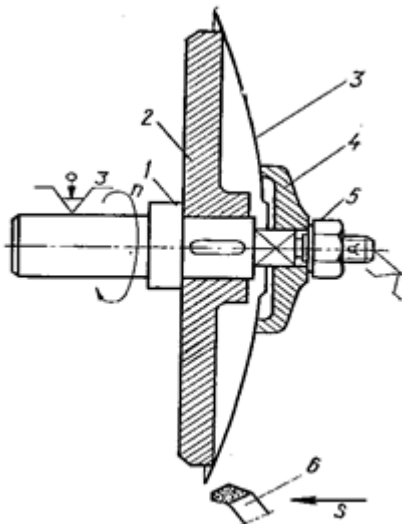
Схема загострювання диску на токарно-гвинторізному верстаті: 1 – оправка; 2 – планшайба; 3 – диск; 4 – шайба; 5 – гайка; 6 – різець.
